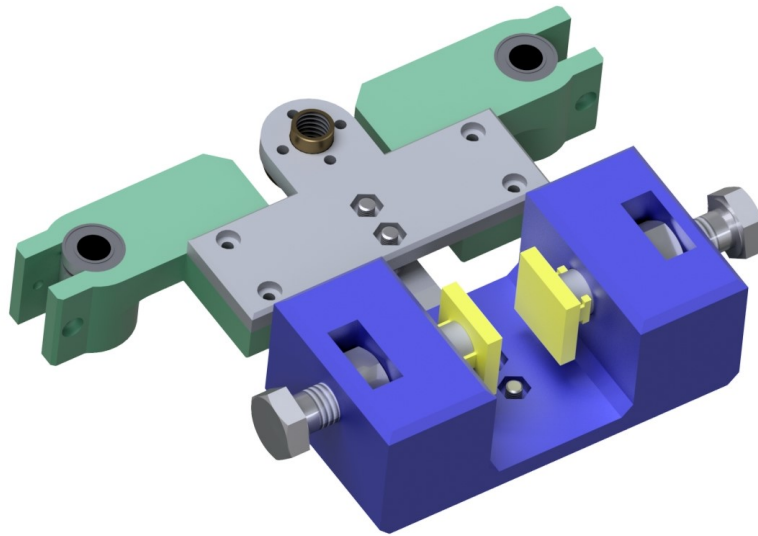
Isométrico del diseño final del módulo de pinza móvil de la máquina de ensayos, primera iteración
